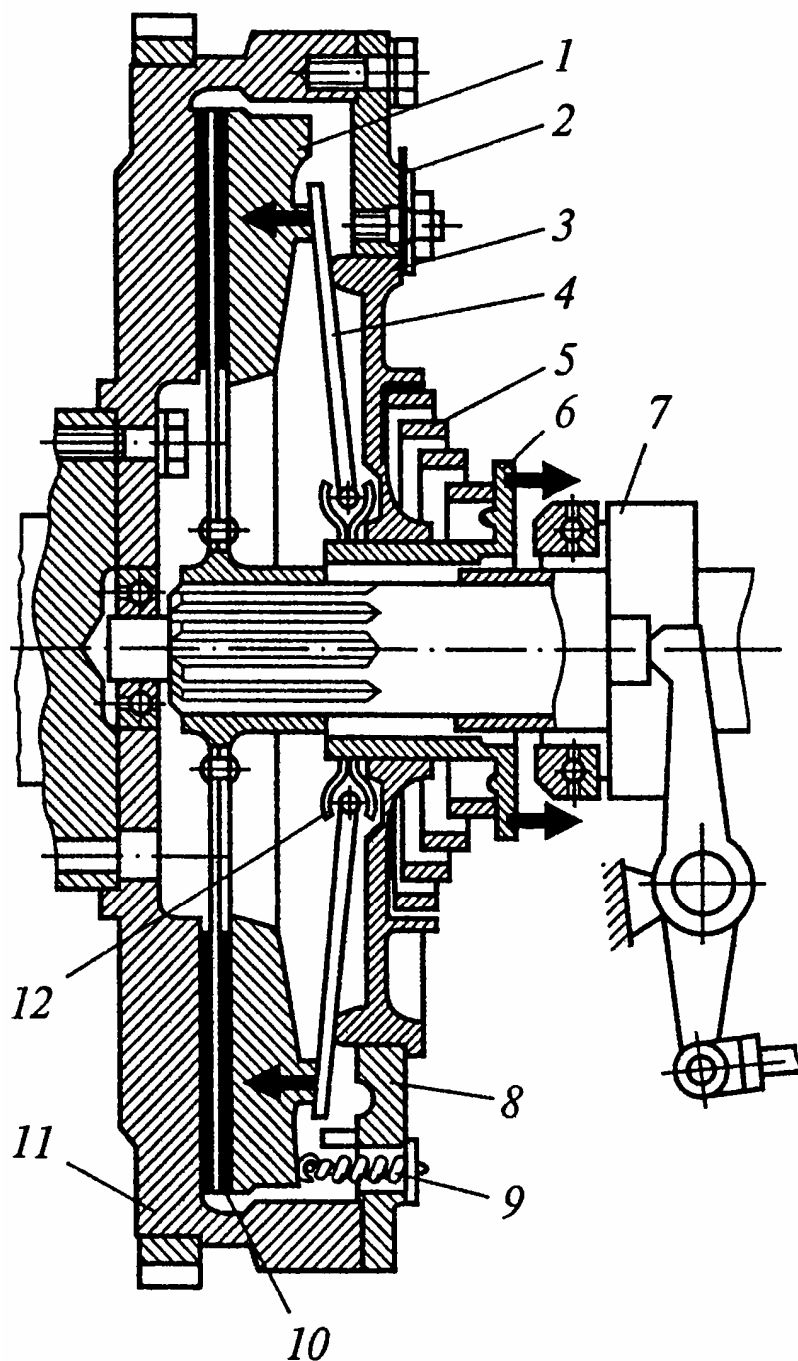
Однодисковое сцепление с конической пружиной грузового автомобиля МАЗ:
